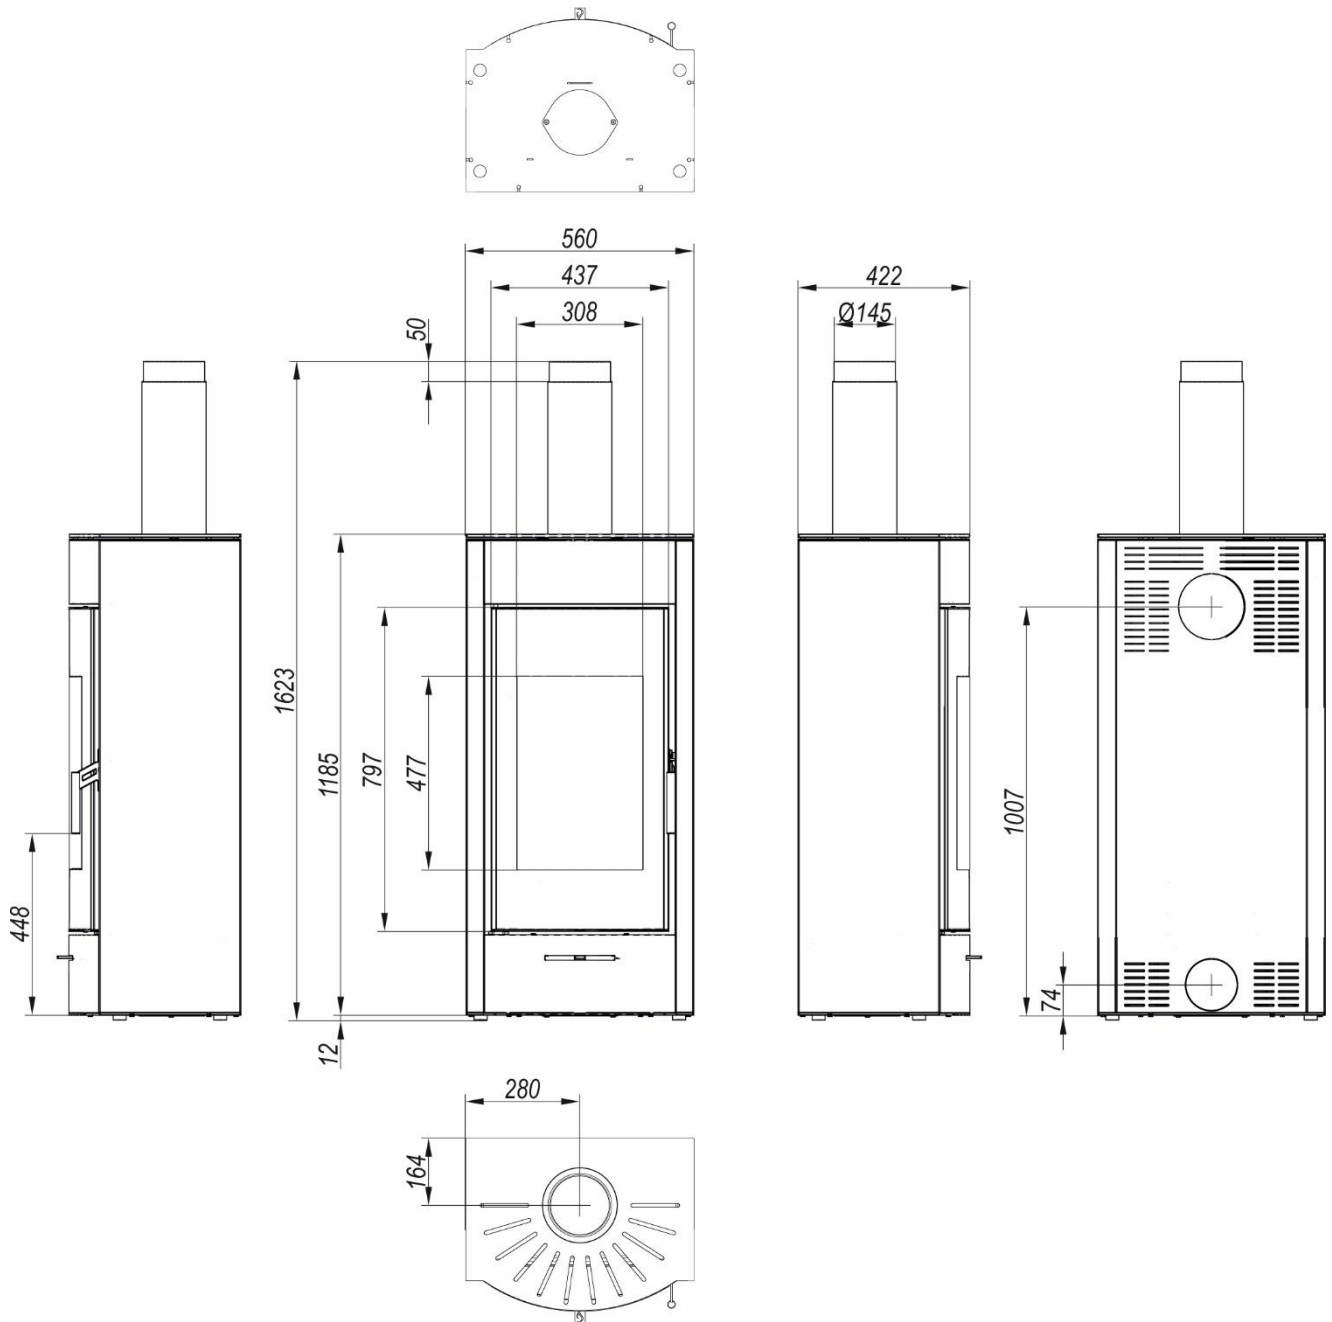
Dimensioni della stufa AIR WOOD ORCHIDEA (in mm).
